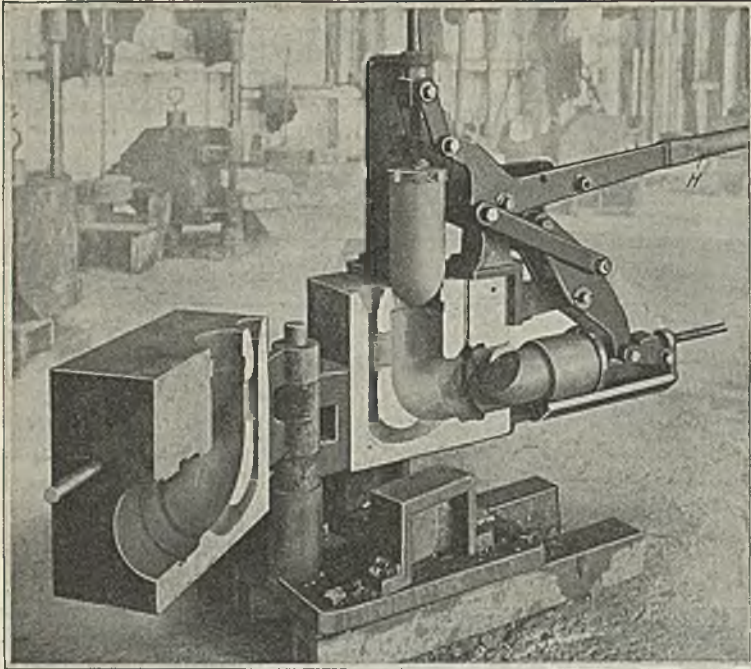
Formmaschine für Viertel-Krümmen unmittelbar nach dem Ausheben des Gußstücks.
